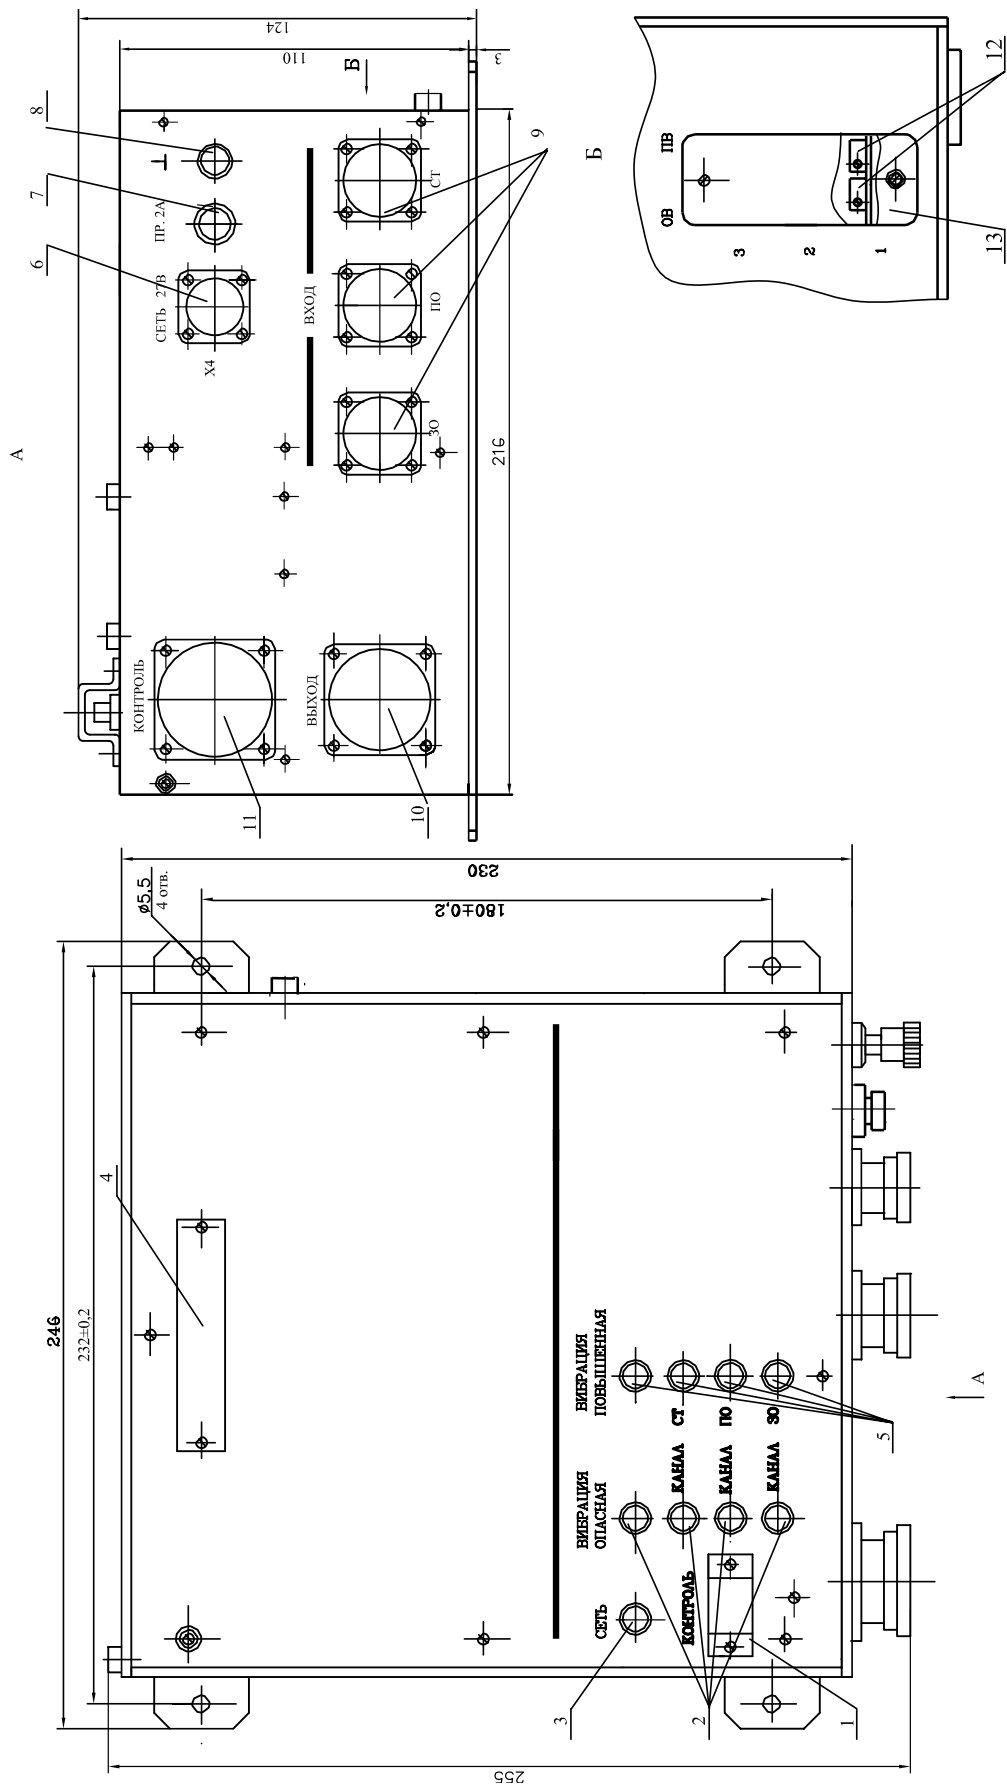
Габаритно-установочные размеры блока БЭ-38-28
